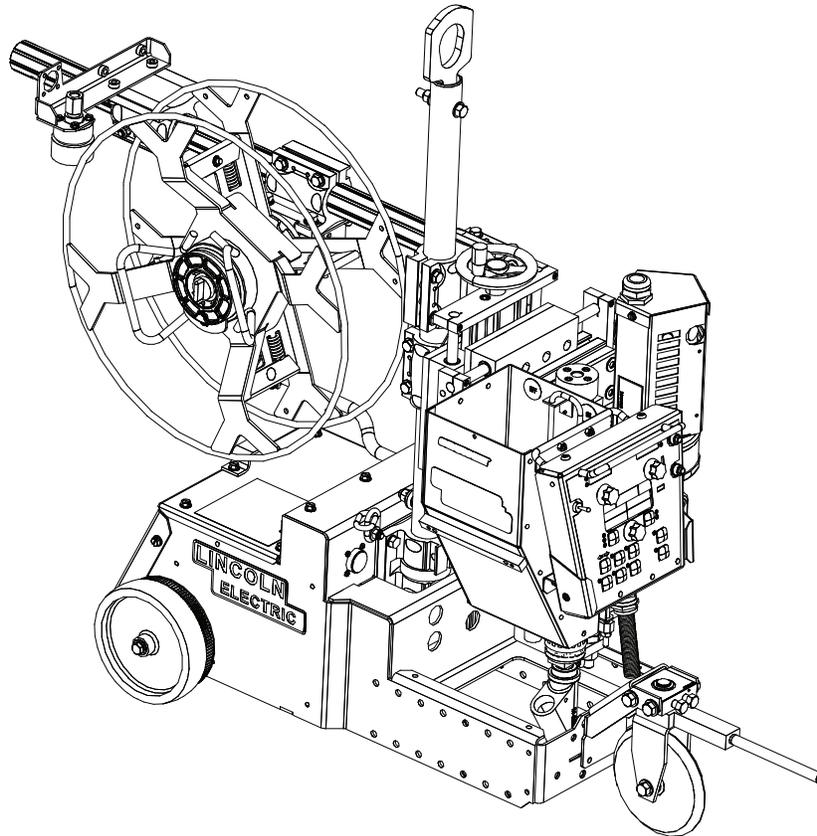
JUNTA DE TPO, 3 RODAS, RODA DE DIREÇÃO, VISTA FRONTAL
